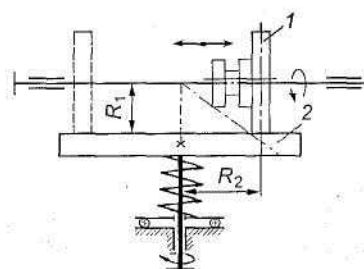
Лобовой вариатор: 1 — ведущий каток; 2 — ведомый каток
